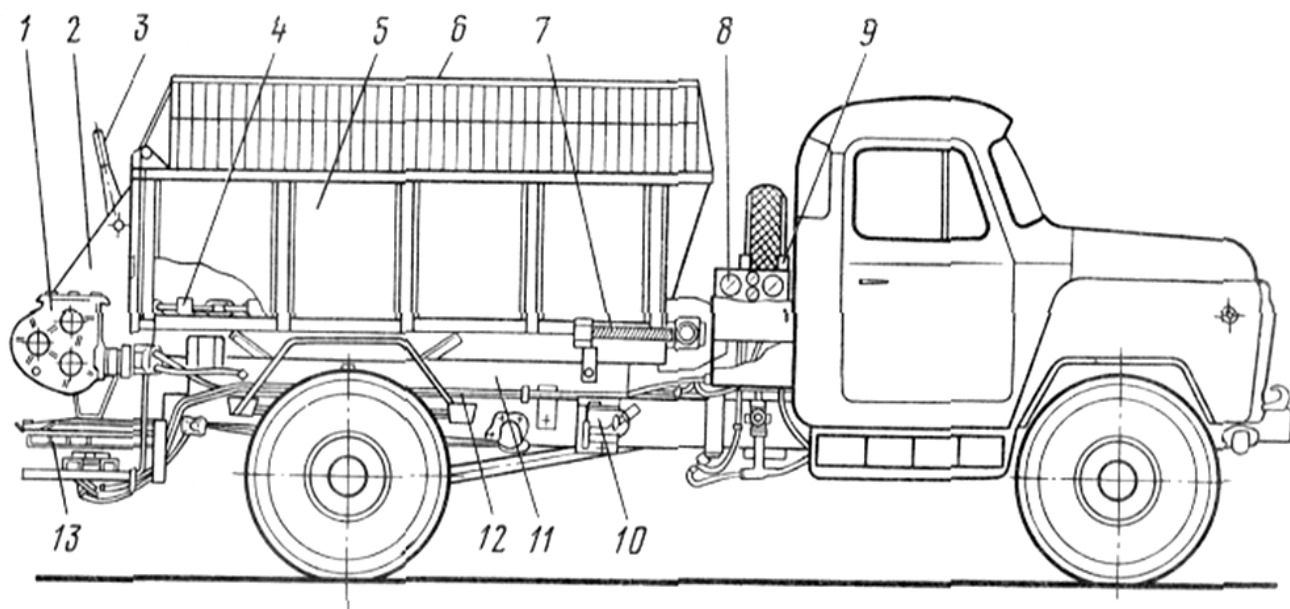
Разбрасыватель универсальный КО – 104А
